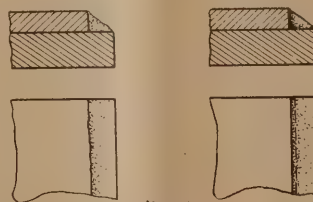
Kehlschweißung in einem Guß. Kehlschweißung in 2 Absätzen.
